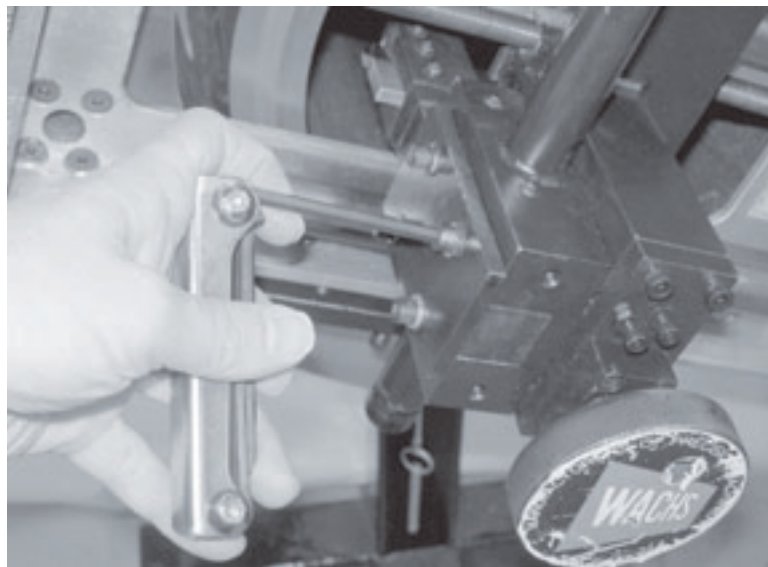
Для установки резцедержателя можно протянуться через суппорт и вставить держатель в переднюю часть резцовой головки.
